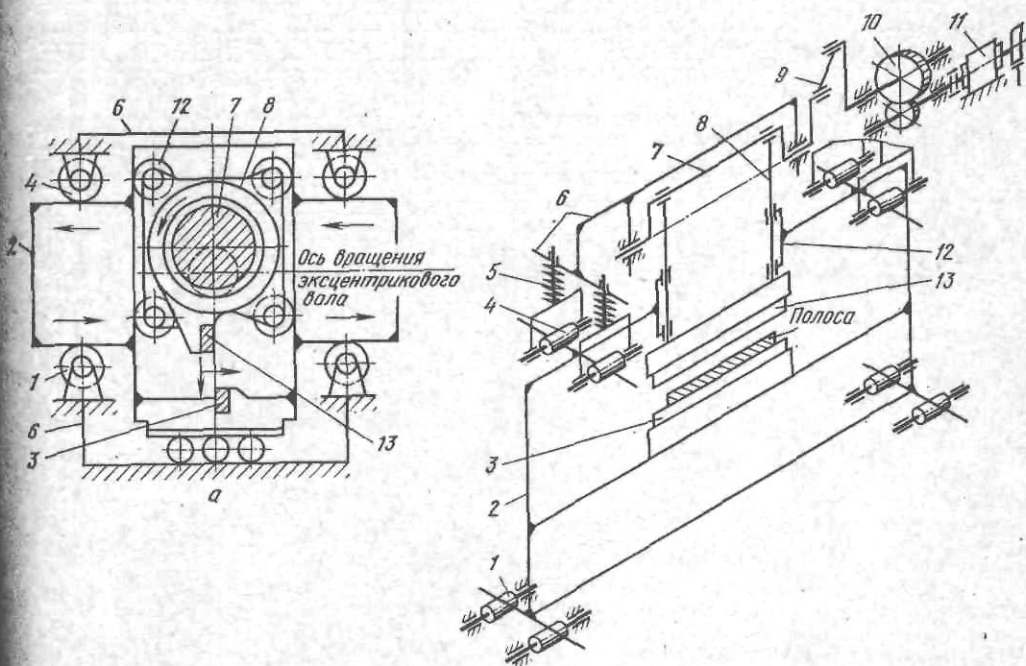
Конструктивно-кинематическая схема летучих ножниц с поступательным движением ножей резки полосы и гнутых профилей:
